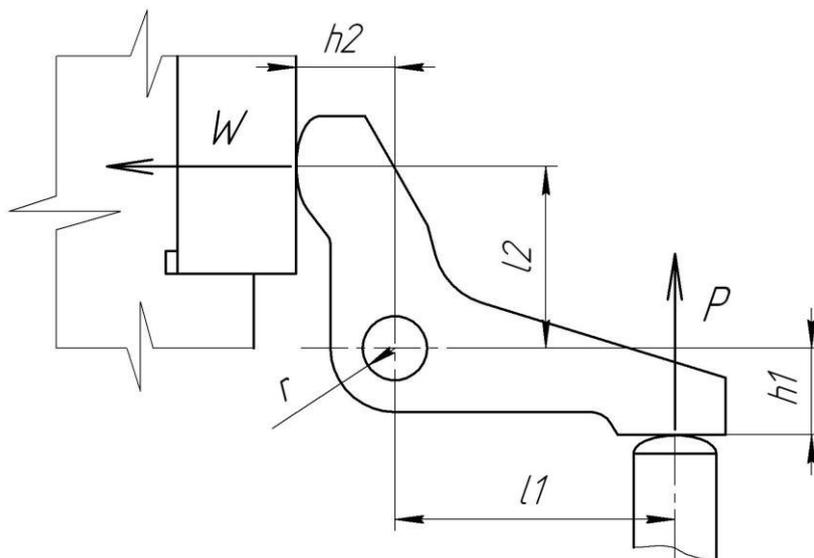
Двухплечевой угловой рычажный зажимной механизм
